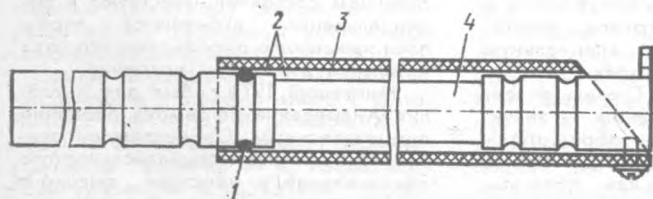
Модернизированный трубчатый разрядник: 1 — резиновый уплотнитель; 2 — кремнийорганическое заполнение и покрытие; 3 — полиэтиленовый чехол; 4 — бакелитовая трубка разрядника
